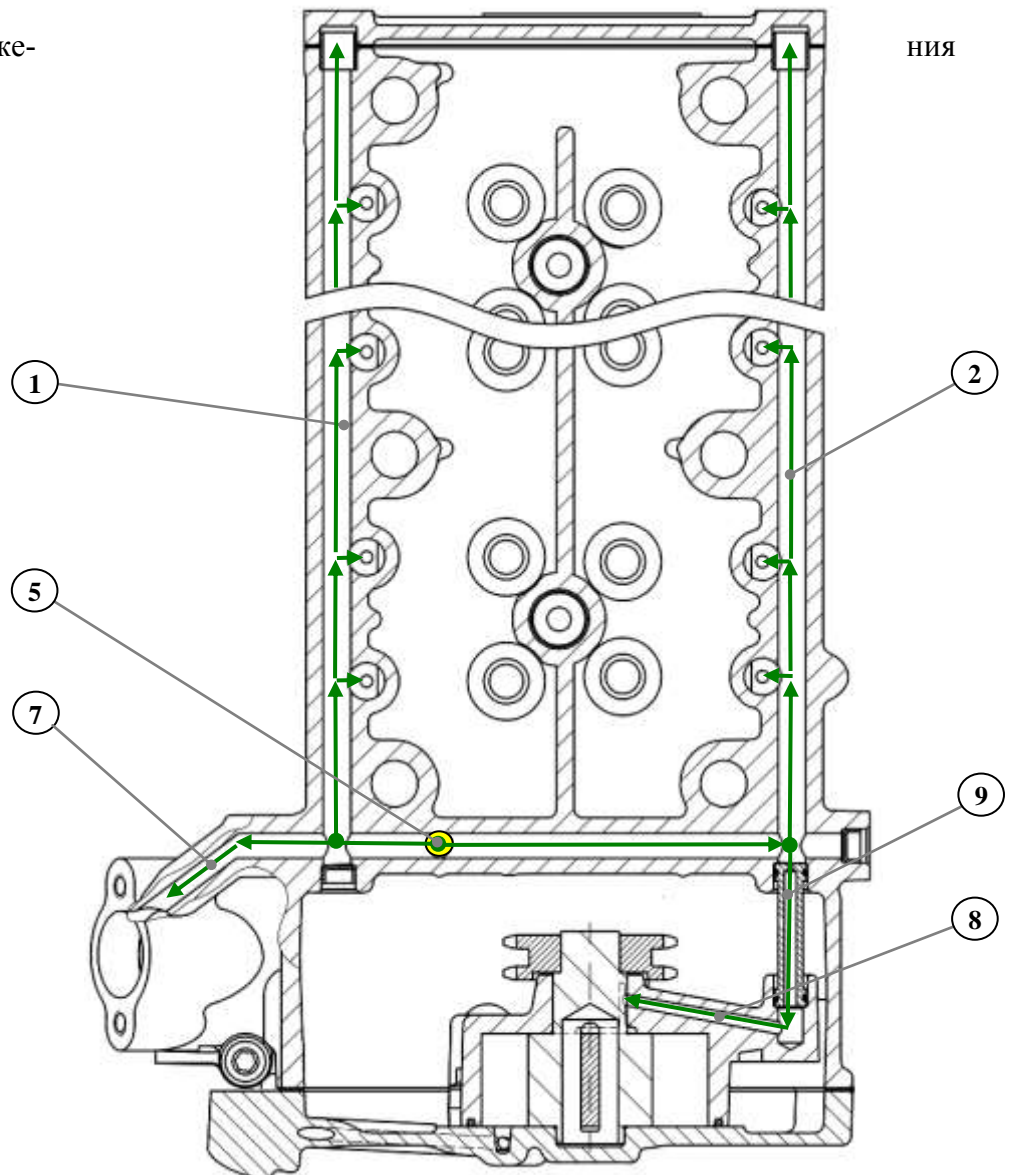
Схема подачи смазочного масла к деталям привода ГРМ:
